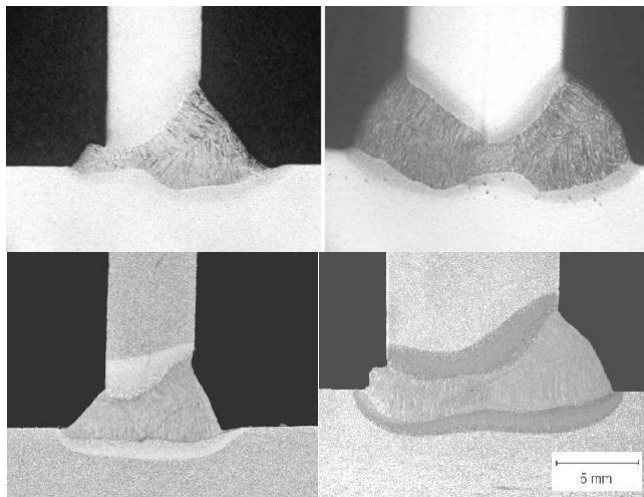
Schweißbilder mittels Traktor hybridgeschweißter Kehlnähte, oben mit 4 kW Nd:YAG-, unten mit 10 kW Faser-Laser
